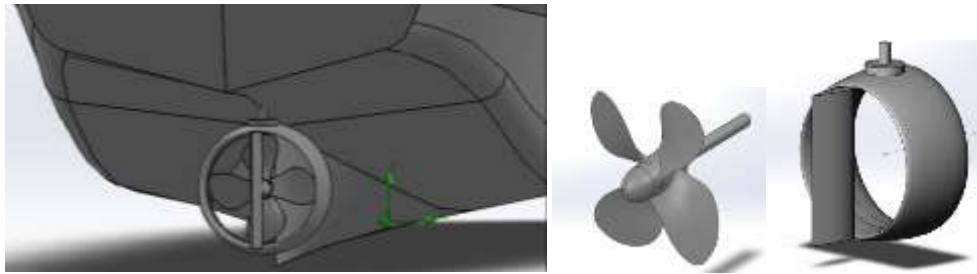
3D-модели поверхности корпуса судна, гребного винта и насадки
